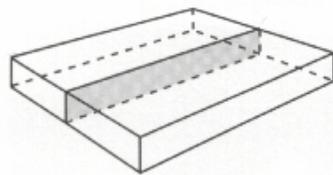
ANSI/AWS A3.0, *Standard Welding Terms and Definitions
